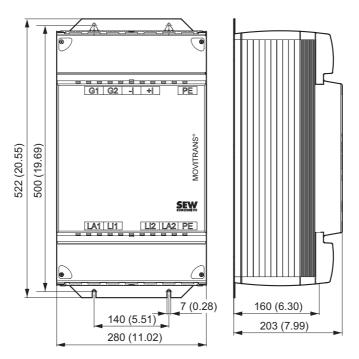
Dimensões do MOVITRANS[®] de tamanho 4, dimensões em mm (in)
